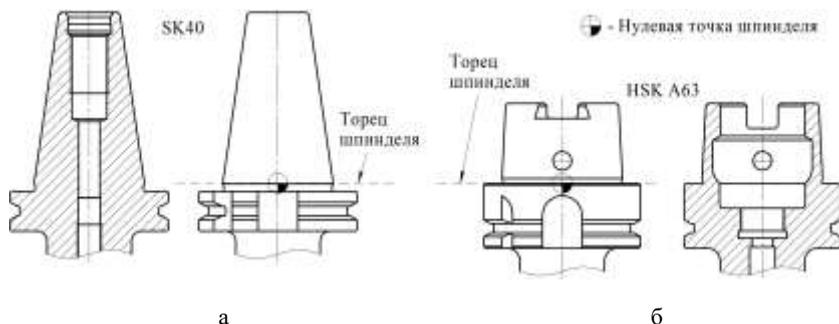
Нулевая точка шпинделя фрезерного станка на оснастке:
